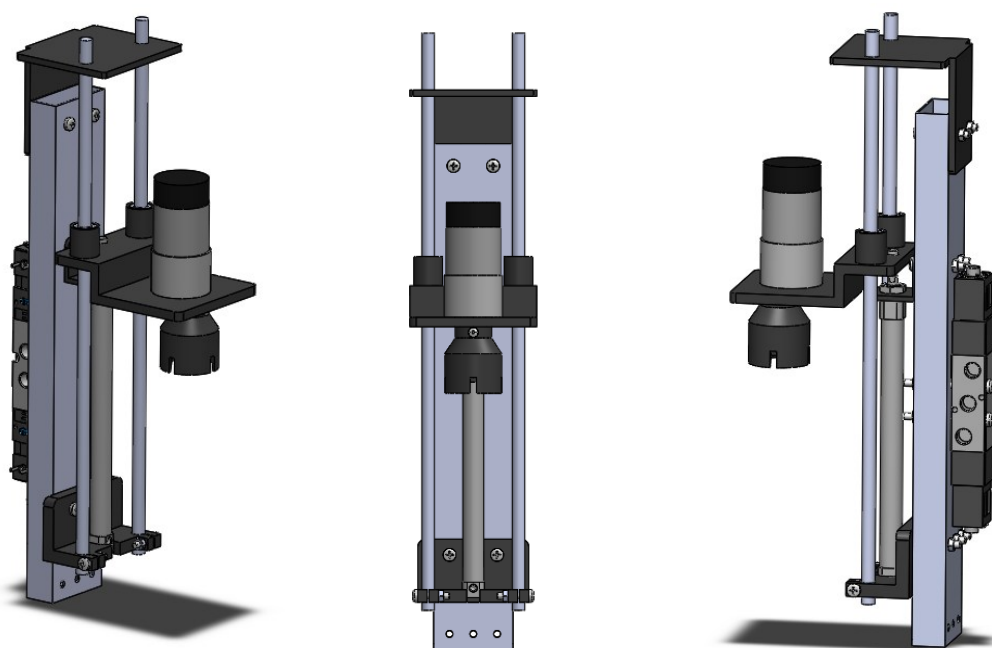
a) Držač cilindra; b) Držač za aluminijske vodilice
